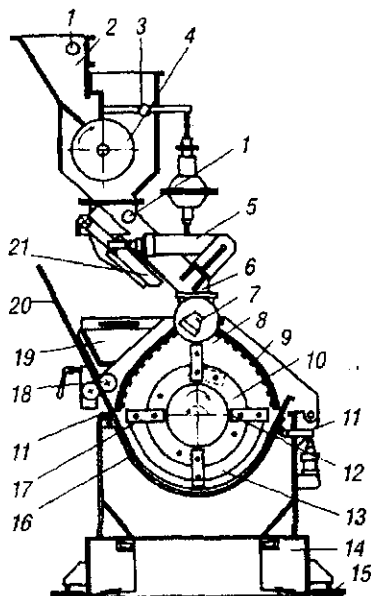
Основные узлы молотковой дробилки серии 20: 1 – датчики уровня; 2 – приемный патрубок; 3 – электропневматический регулирующий клапан; 4 – барабан питателя; 5 – пневмоцилиндр; 6 – нижний патрубок магнитного сепаратора; 7 – поворотный клапан; 8 – камера дробления (верхняя); 9 – дека; 10 – ротор монолитный; 11 – пневматическое устройство для герметизации, фиксации сита; 12 – ось молотков; 13 – камера дробления (нижняя); 14 – станина; 15 – виброопоры; 16 – второе сито; 17 – молоток; 18 – устройство автоматической смены сита; 19 – сборник металломагнитных примесей; 20 – первое сито; 21 – магнитный сепаратор
